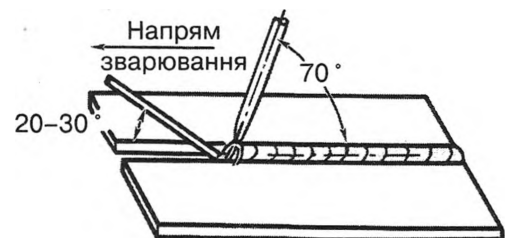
Зварювання з подачею присаджувального матеріалу в дугу
